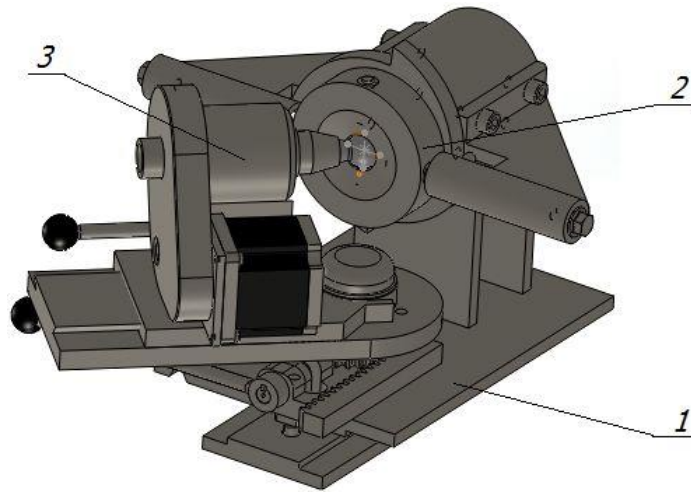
Технологічна оснастка для статико-імпульсного зміцнення ППД неповної сферичної поверхні пальця кульової опори: 1 – платформа; 2 – інструментальна головка для статико-імпульсного деформування; 3 – поворотний пристрій для закріплення заготовки
